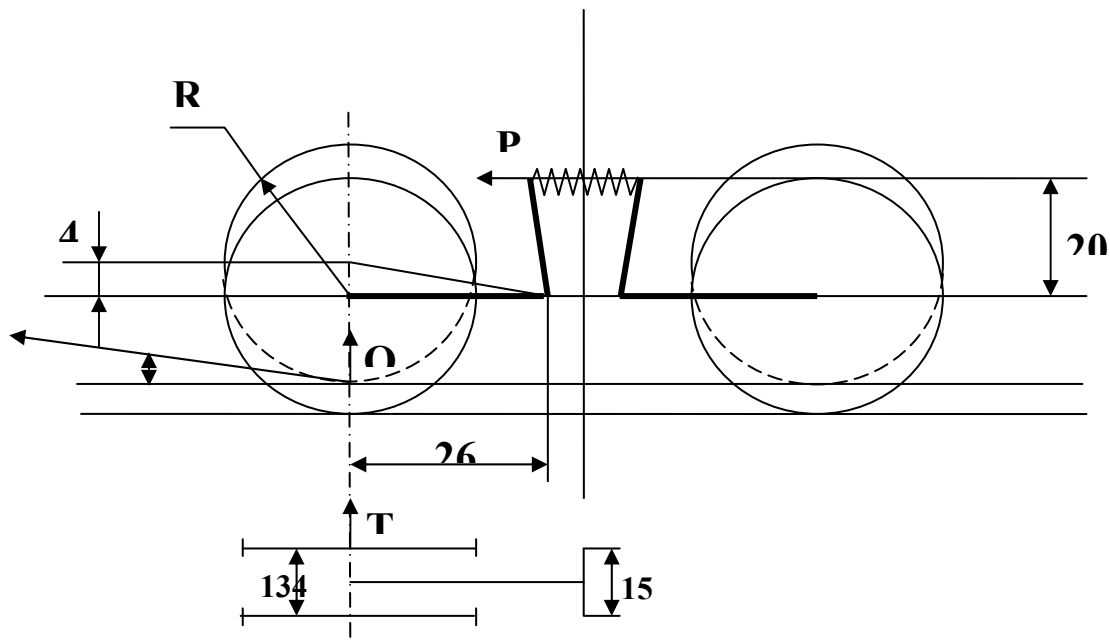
Расчетная схема определения нагрузок на втулки балансира
